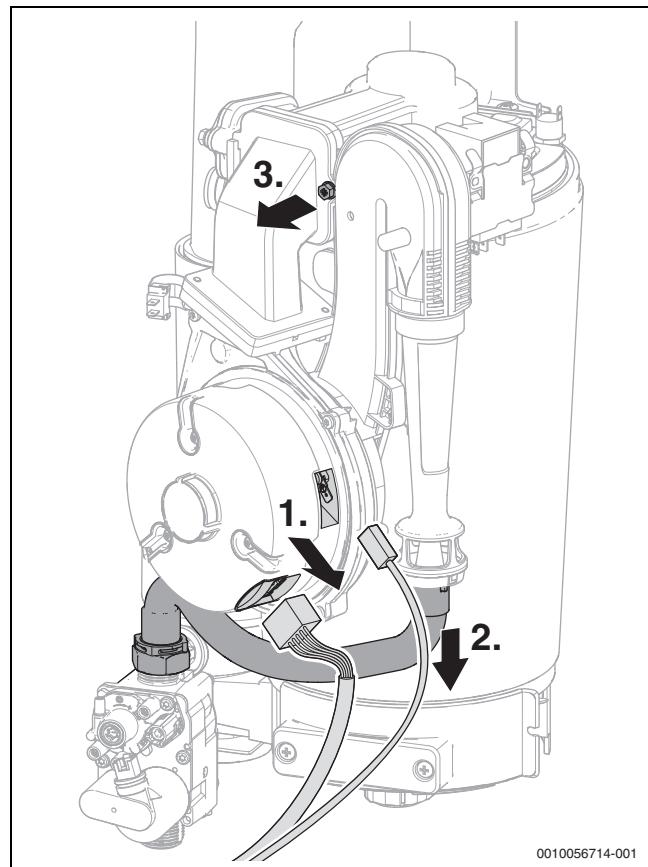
Stecker und Gasschlauch abziehen, Schraube lösen
